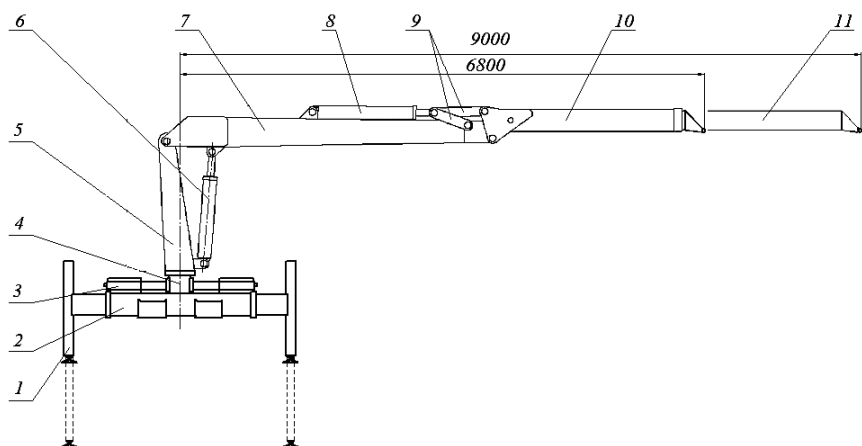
Устройство крана-манипулятора: 1 – выдвигаемые опоры; 2 – несущая рама манипулятора; 3 – гидроцилиндры поворота стрелы; 4 – опорно-поворотные устройства; 5 – стойка стрелы; 6 – гидроцилиндр подъема стрелы; 7 – стрела; 8 – гидроцилиндр складывания стрелы; 9 – тяги; 10 – складываемая секция; 11 – выдвигаемая секция
